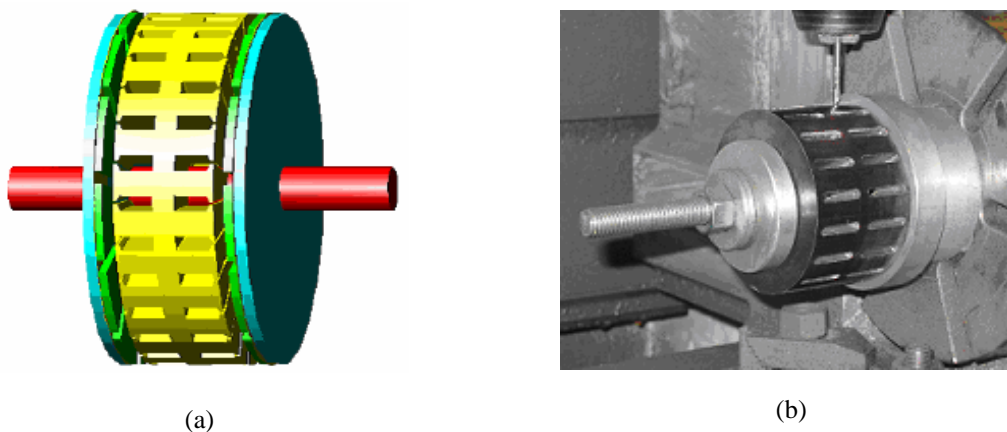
TORUS avec stator en SMC : (a) vue de la machine et (b) fabrication du stator en SMC [37].
